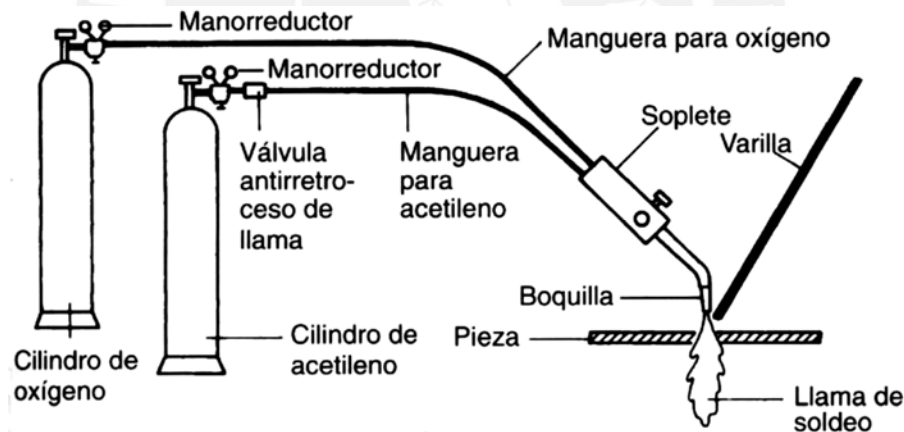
Proceso de soldadura OFW [1]
